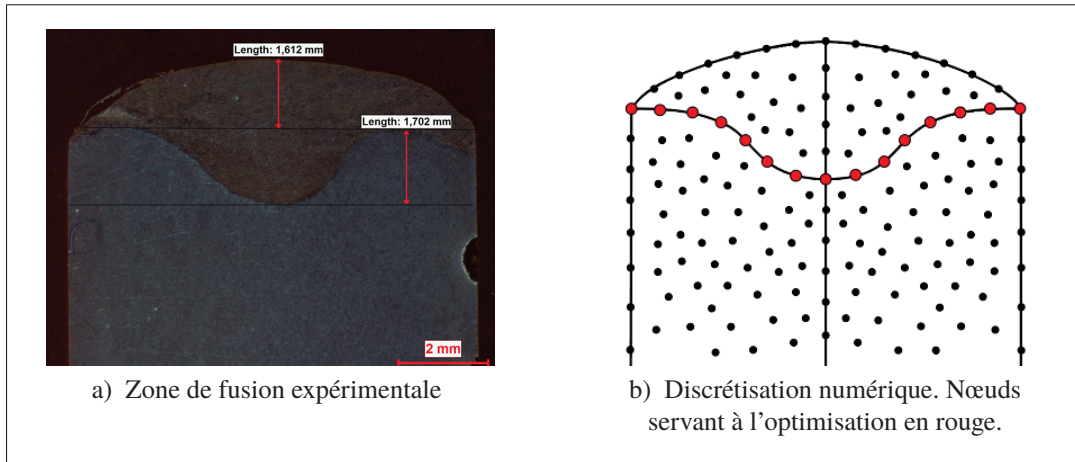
Vues de coupe de la zone de fusion, prises à mi-longueur de la trajectoire de soudure
